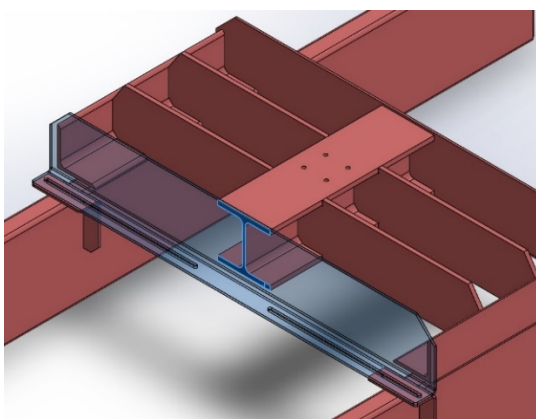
Detalle de las partes de la unión soldada crítica del aparato de carga
